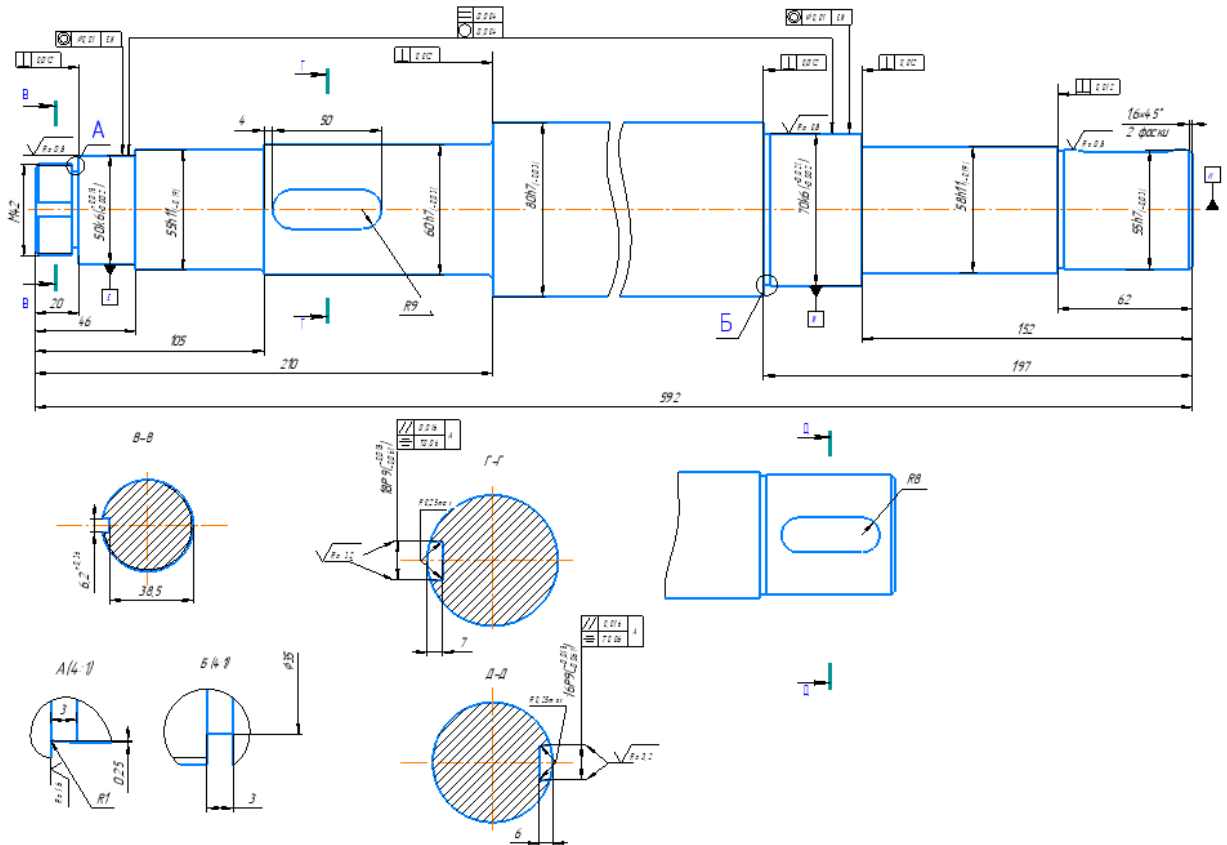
Загальний вигляд деталі «вал черв'ячного редуктора»
